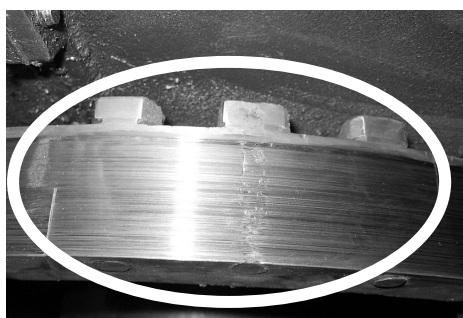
Opotřebovaný sběrný kruh až na hlavy stahovacích šroubů
